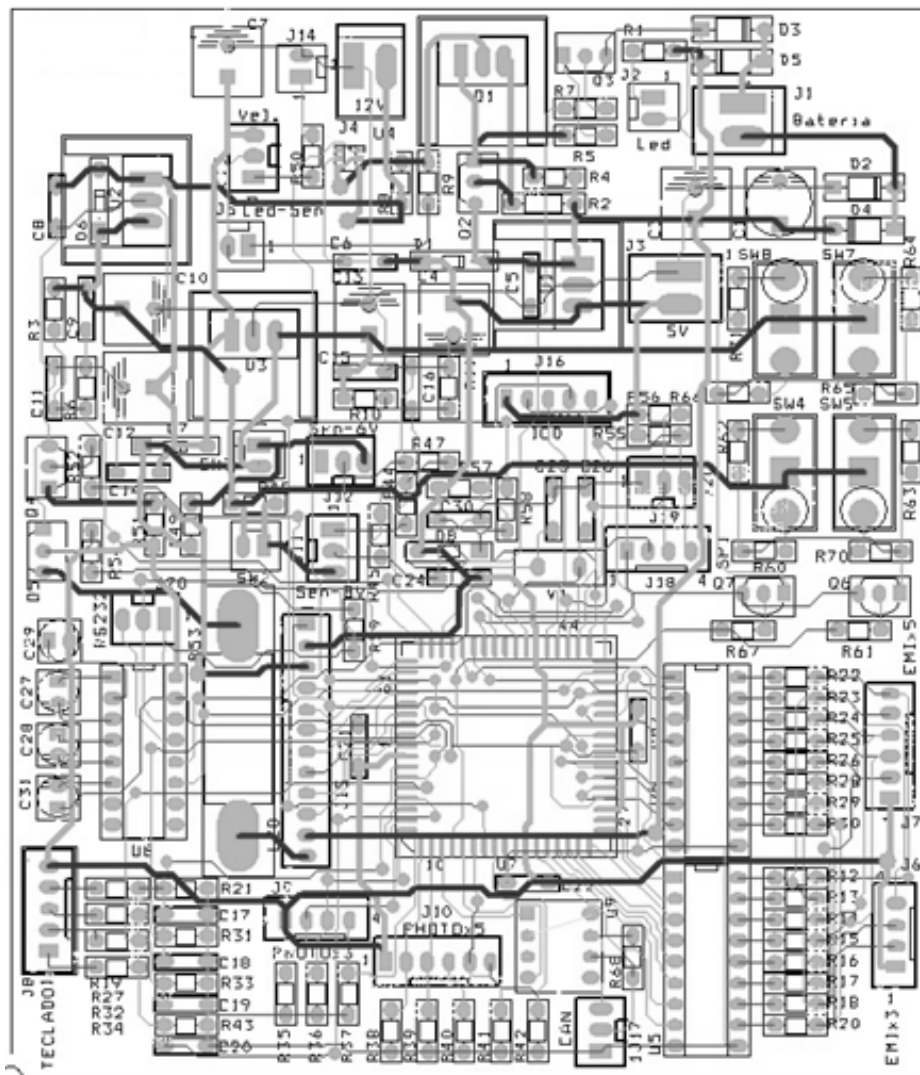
Imagen del diseño del PCB sin planos a tierra
